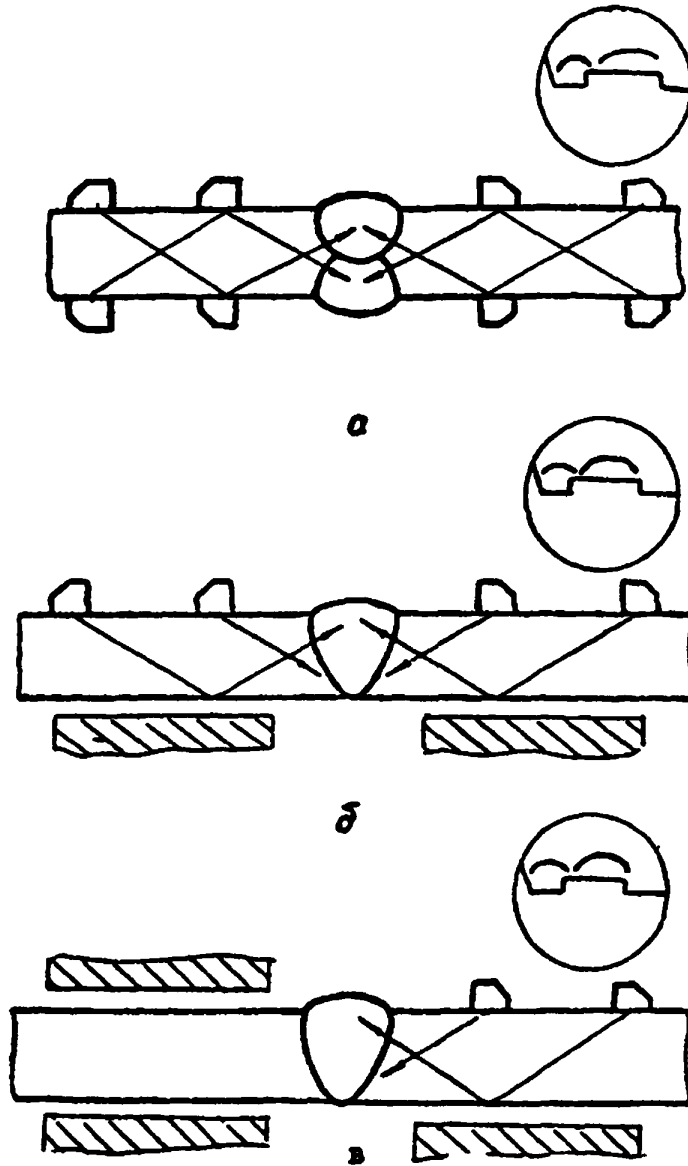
Схемы контроля стыковых сварных соединений без подкладных пластин;
